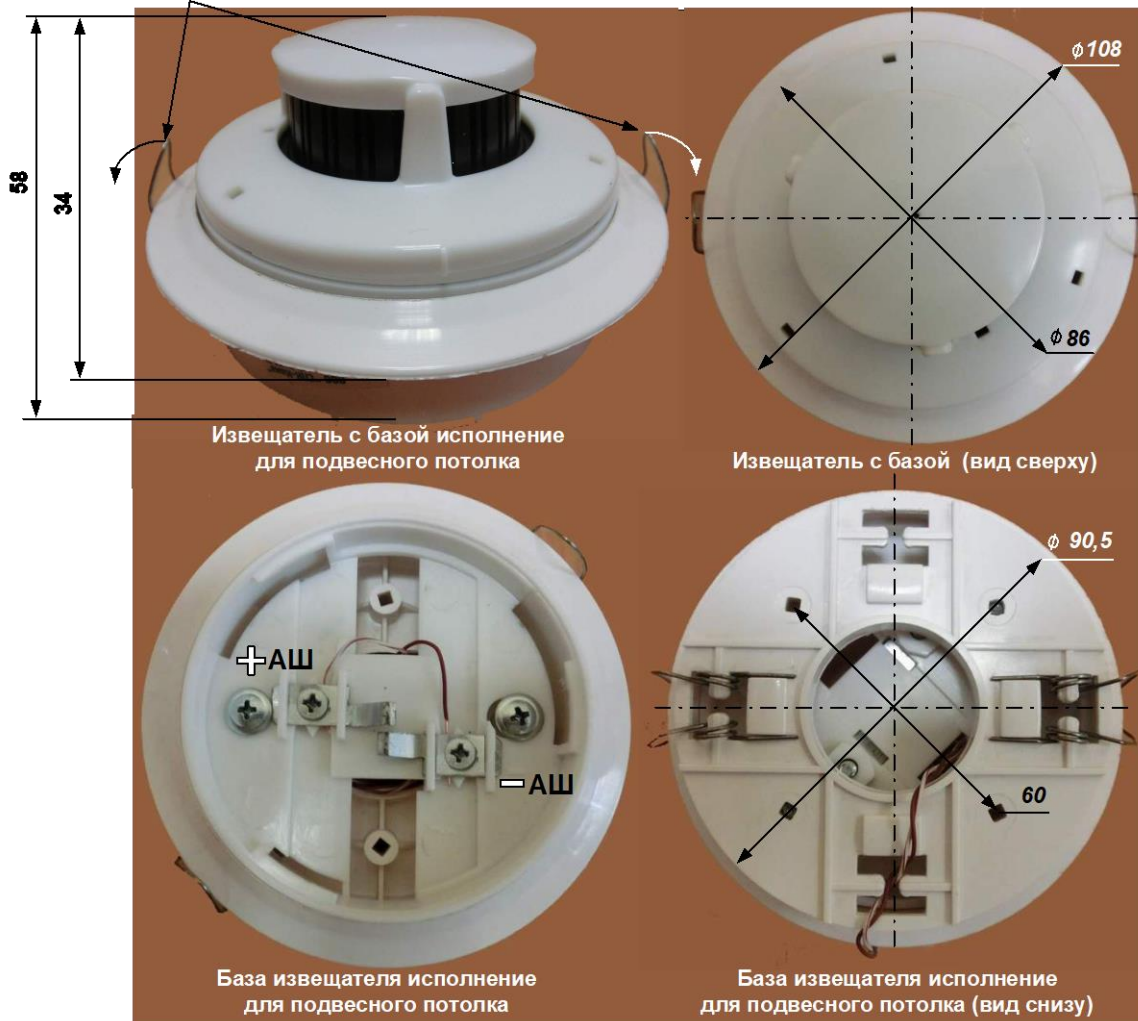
АТИ. Извещатель с базой для подвесного потолка. Габаритные и присоединительные размеры
